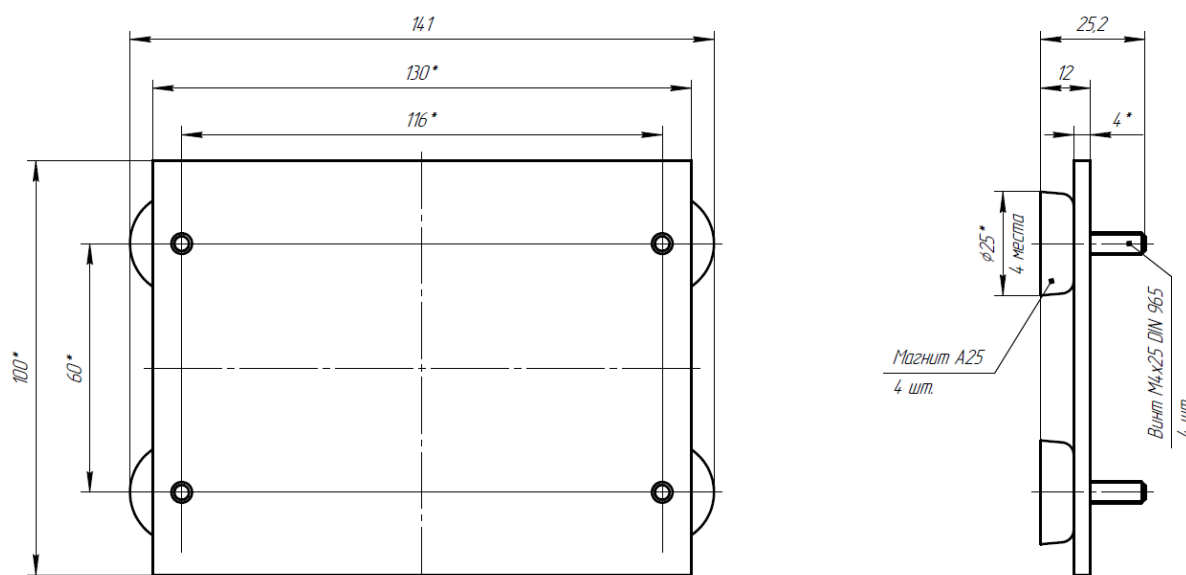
Чертеж монтажной пластины для установки инклинометра на металлическую поверхность
